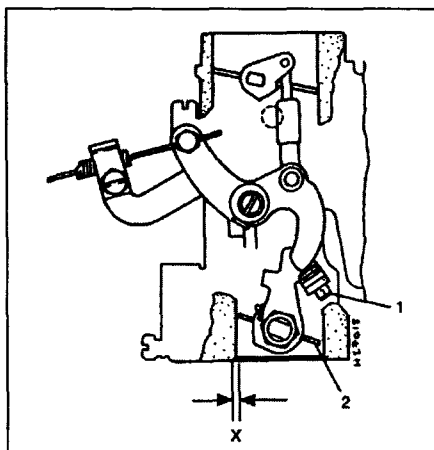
Регулировка пусковых оборотов - с ручным приводом
